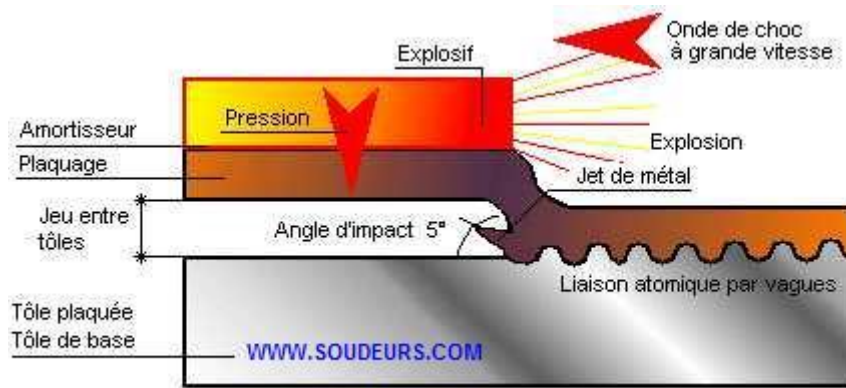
Soudage à l'état solide (explosion)
